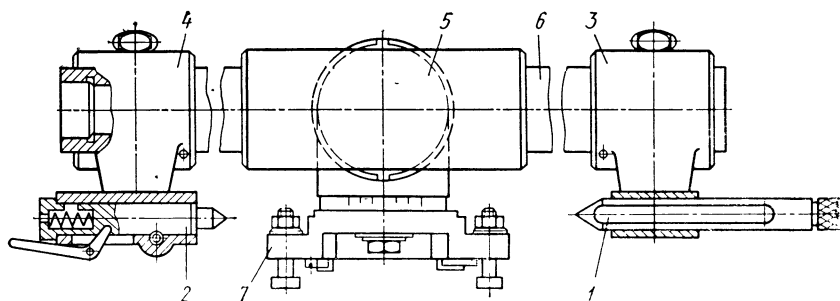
Приспособление для заточки и доводки длинных разверток.
